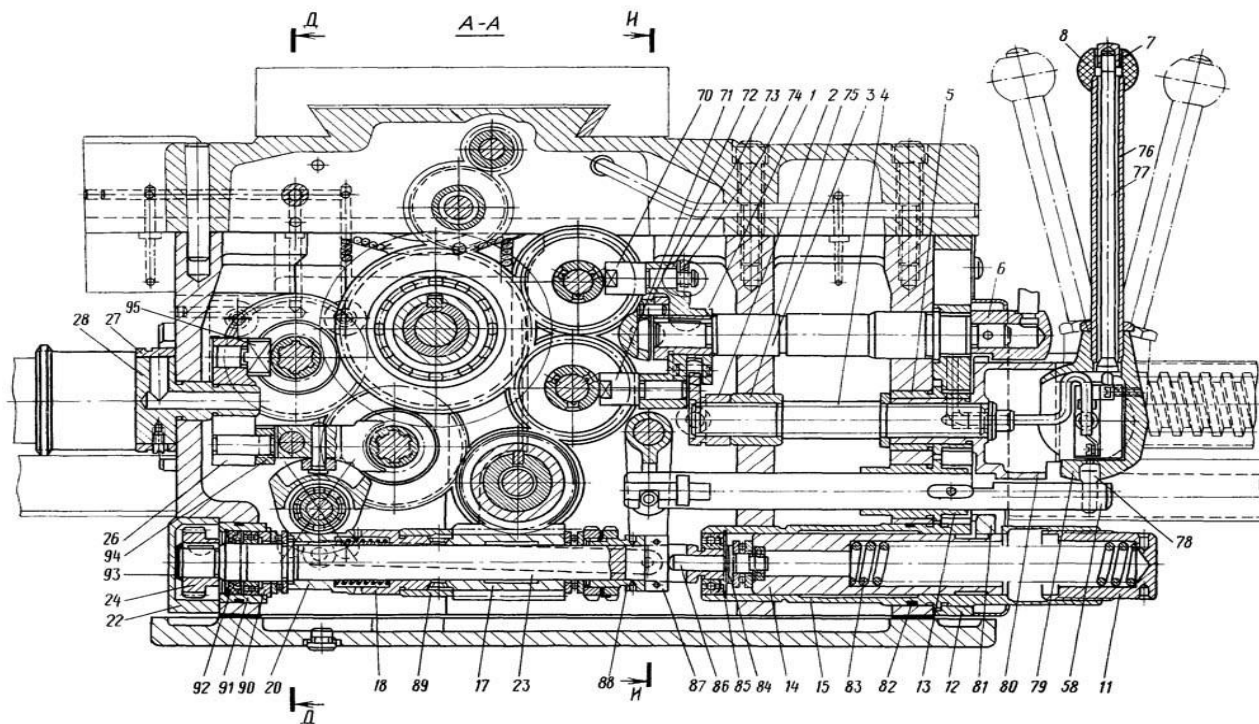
Креслення фартуха токарного верстата 16Б20п.061
